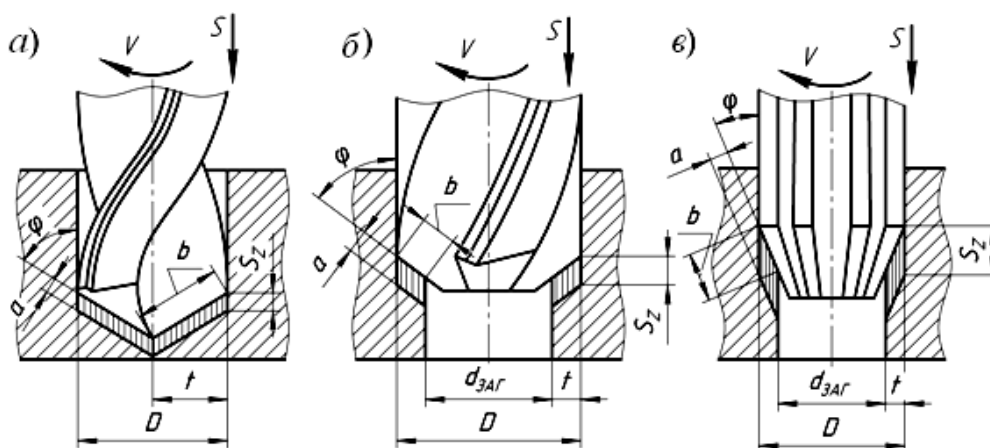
Схемы процессов сверления (а), зенкования (б) и развертывания (в)
